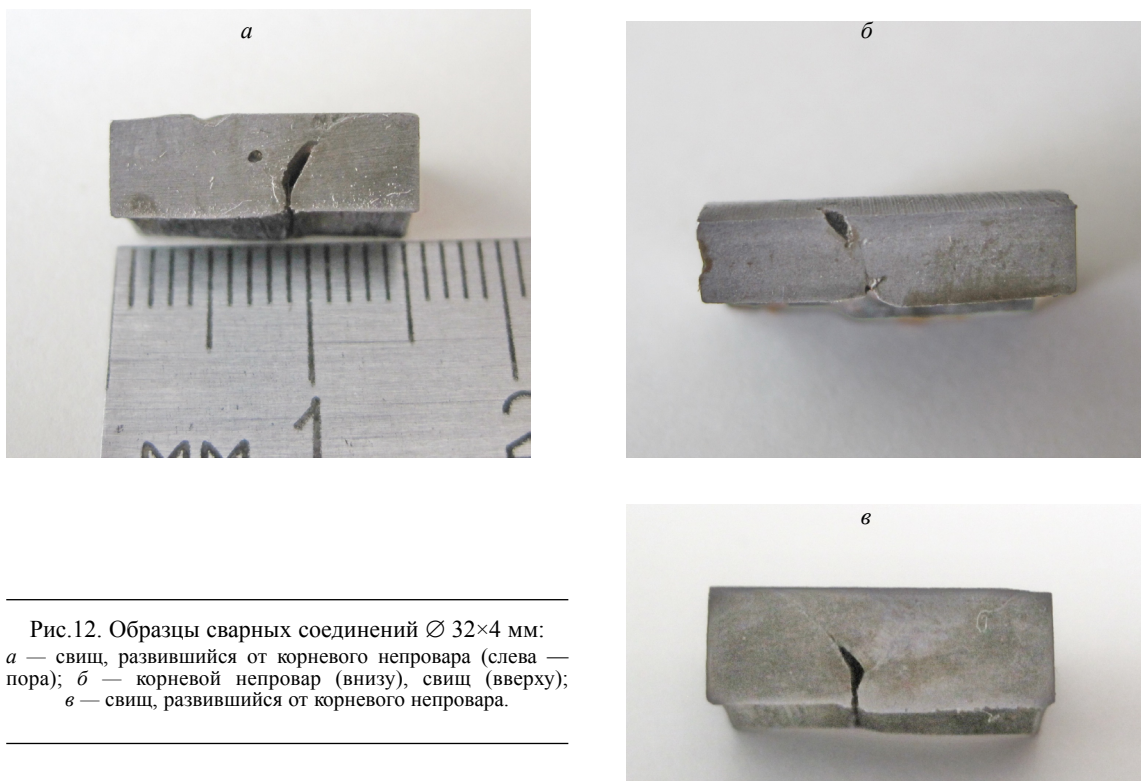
Образцы сварных соединений $\varnothing 32 \times 4$ мм:
